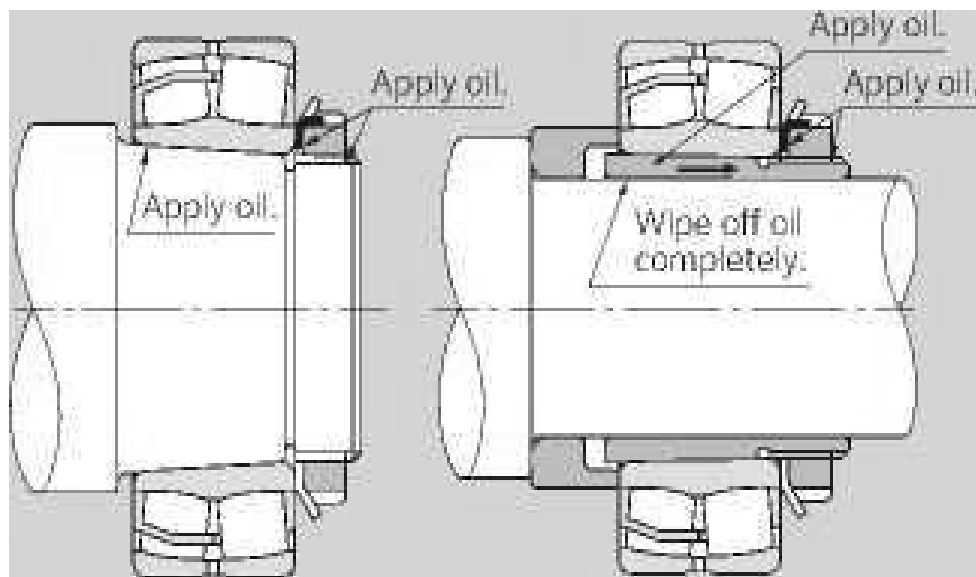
Встановлення конічного підшипника на вал за допомогою контргайки та конічної перехідної втулки
